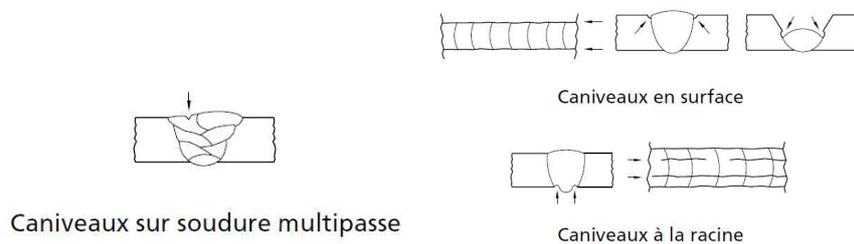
Schémas des différents types de caniveau que l'on peut rencontrer dans une soudure [CSMOFMI, les défauts de soudure]
